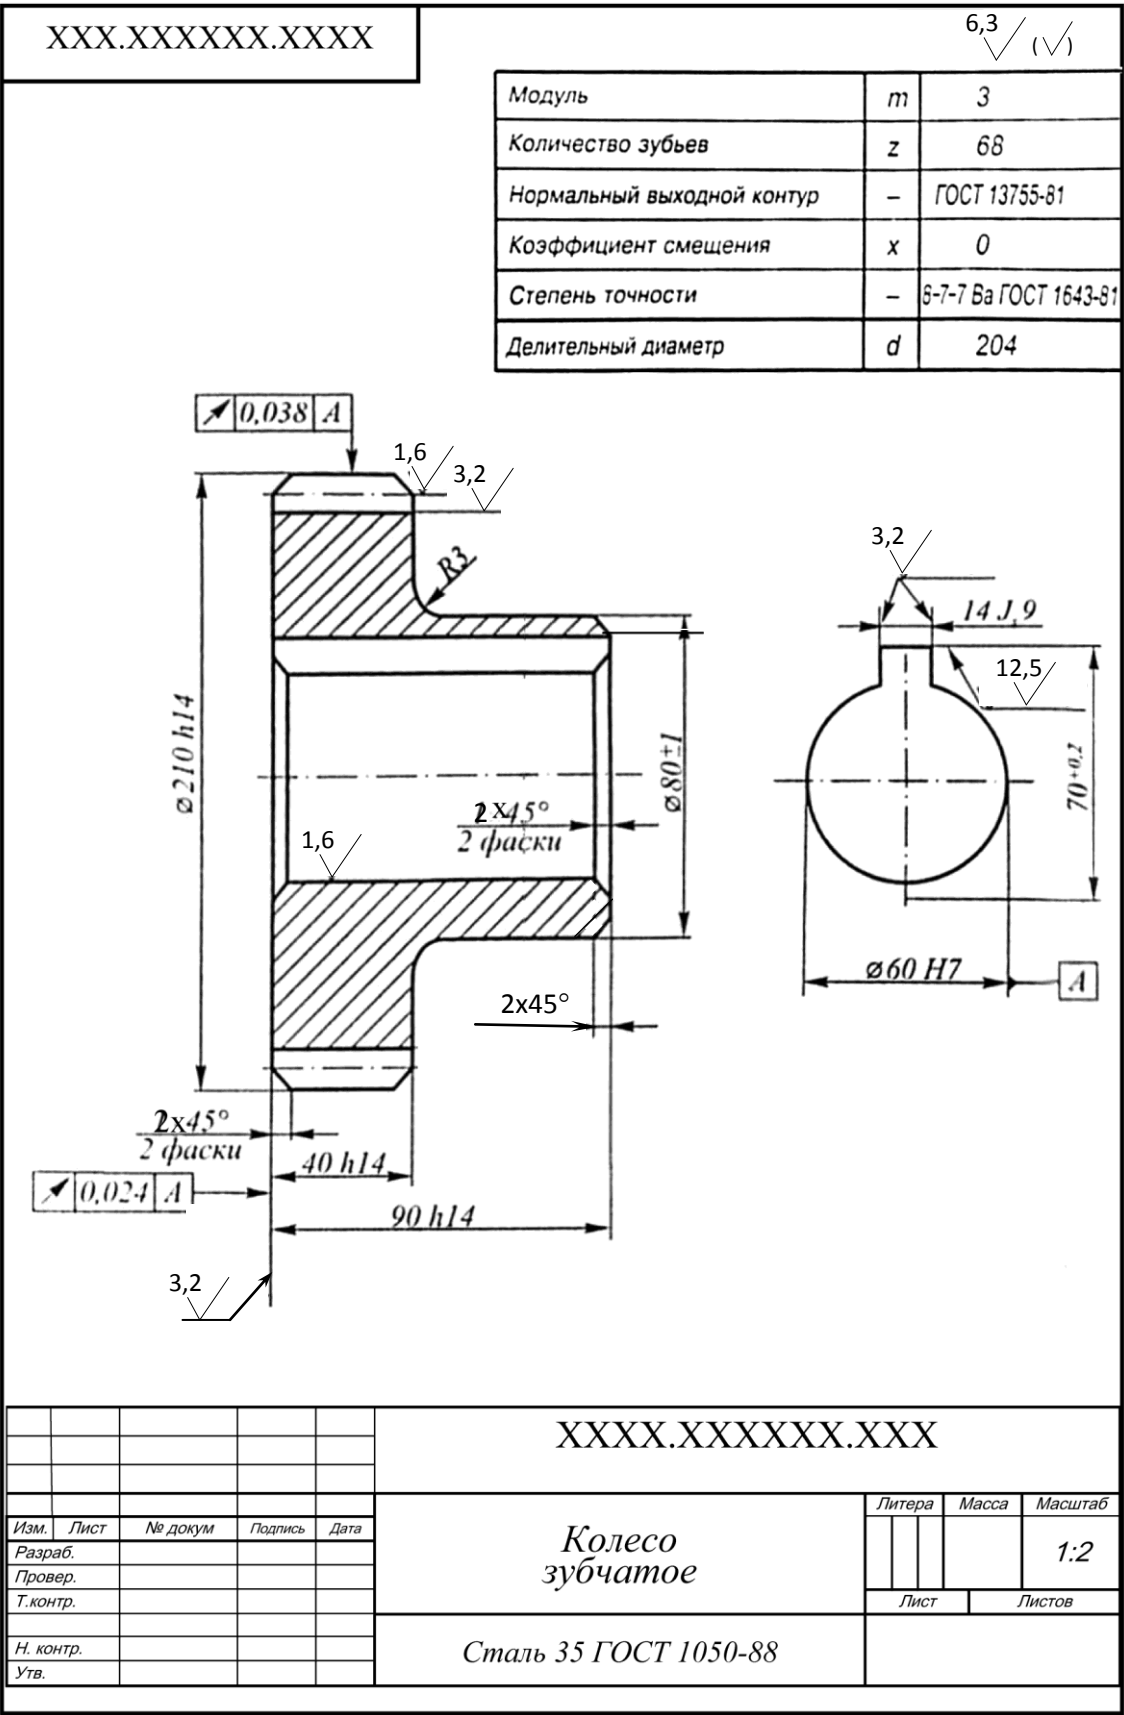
Пример оформления чертежа на колесо зубчатое
